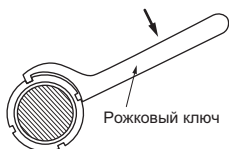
Демонтаж подшипника с помощью рожкового ключа
